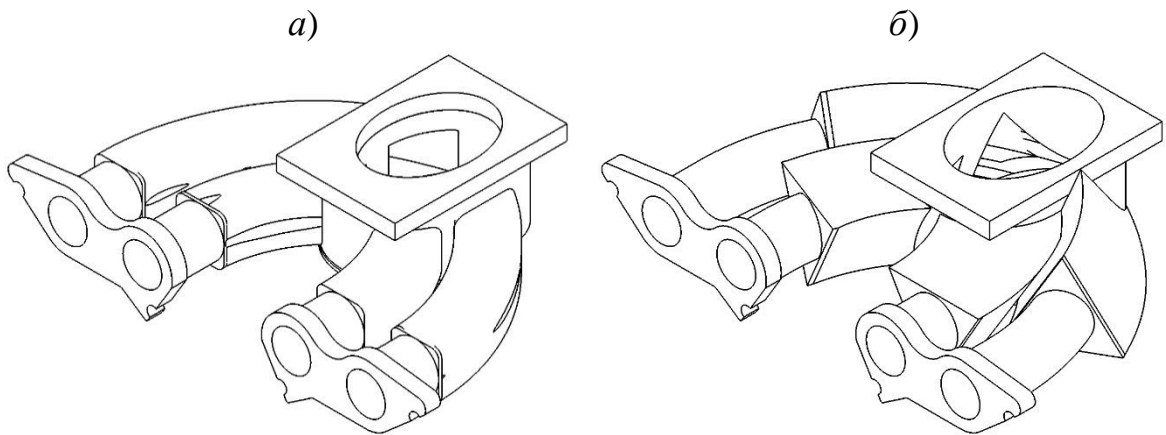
Изометрический вид впускного коллектора двигателя 4Ч 7,6/8,0 (ВАЗ) с каналами в форме квадрата (а) и треугольника (б)
